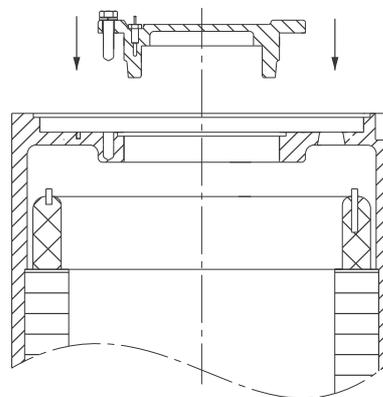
Установка внешней части верхнего подшипника на кронштейн электродвигателя
